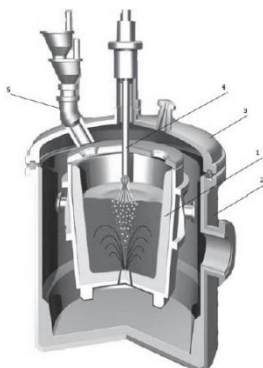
Схема камерного вакууматора VD/VOD: 1 – сталеразливочный ковш; 2 – вакуумная камера; 3 – крышка вакуумной камеры; 4 – кислородная фурма; 5 – устройство для подачи сыпучих материалов
